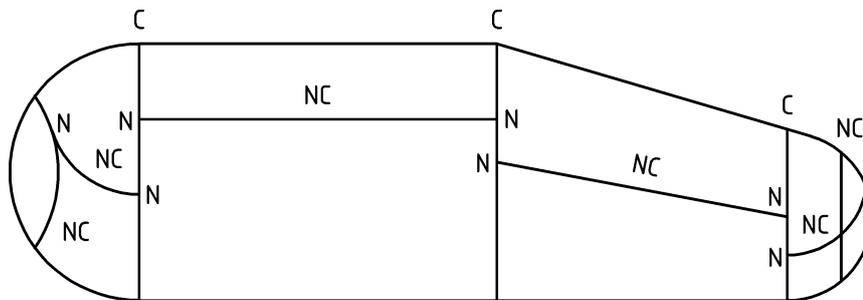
Symbole für Schweißnaht-Positionen
